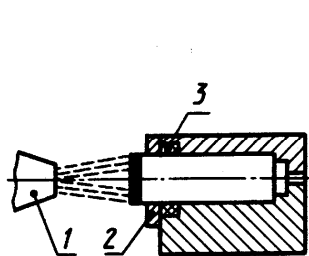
Пытливое закрепление напыляемых деталей в однопозиционном приспособлении: 1-распылительная головка; 2-сменная вставка; 3-уплотнительная прокладка
